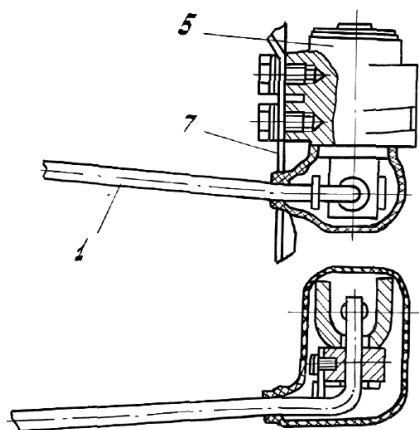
Упруго-передаточный механизм регулятора торсионного типа (ВАЗ): 1 – торсион; 5 – регулятор; 7 – кронштейн крепления
